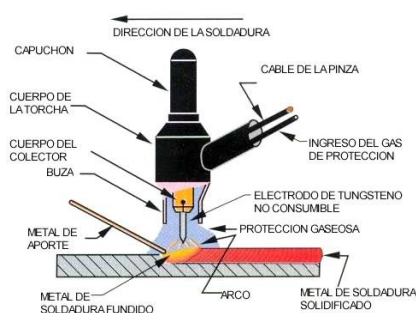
Esquema del proceso de soldadura TIG.
